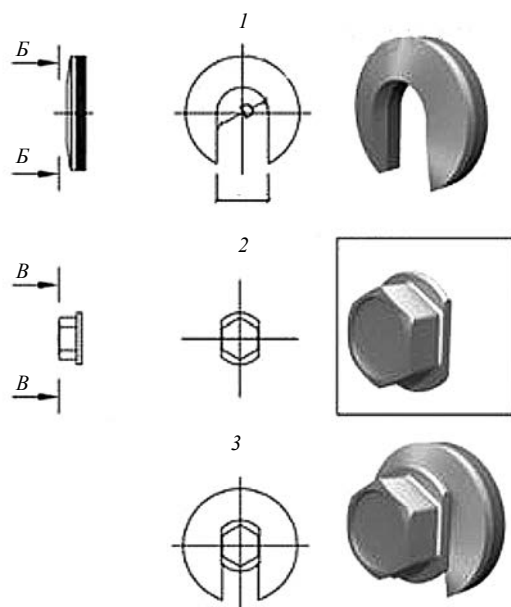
, с. Модель легкосъёмного болта ЛСК компании ООО «Металл Профиль»: 1 — сточенная шайба для самореза; 2 — сточенный фланец головки самореза; 3 — общий вид головки самореза со сточенным фланцем и сточенной шайбой самореза
